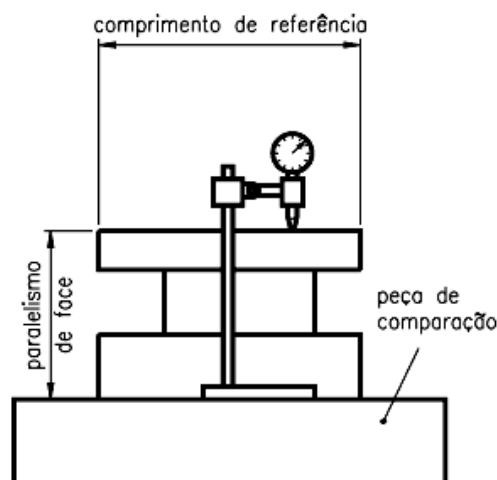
Desenho representativo da forma correta de medir o paralelismo.
